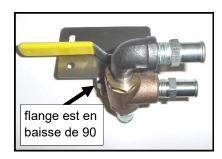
(assemblage de la valve du dérivateur et du support)
